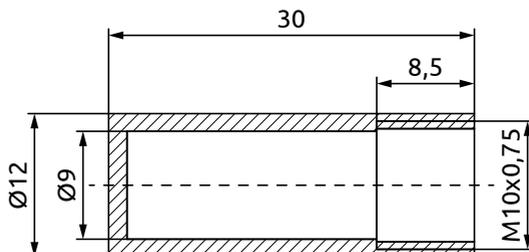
Габаритные размеры защитного колпачка HTE Cap.02
